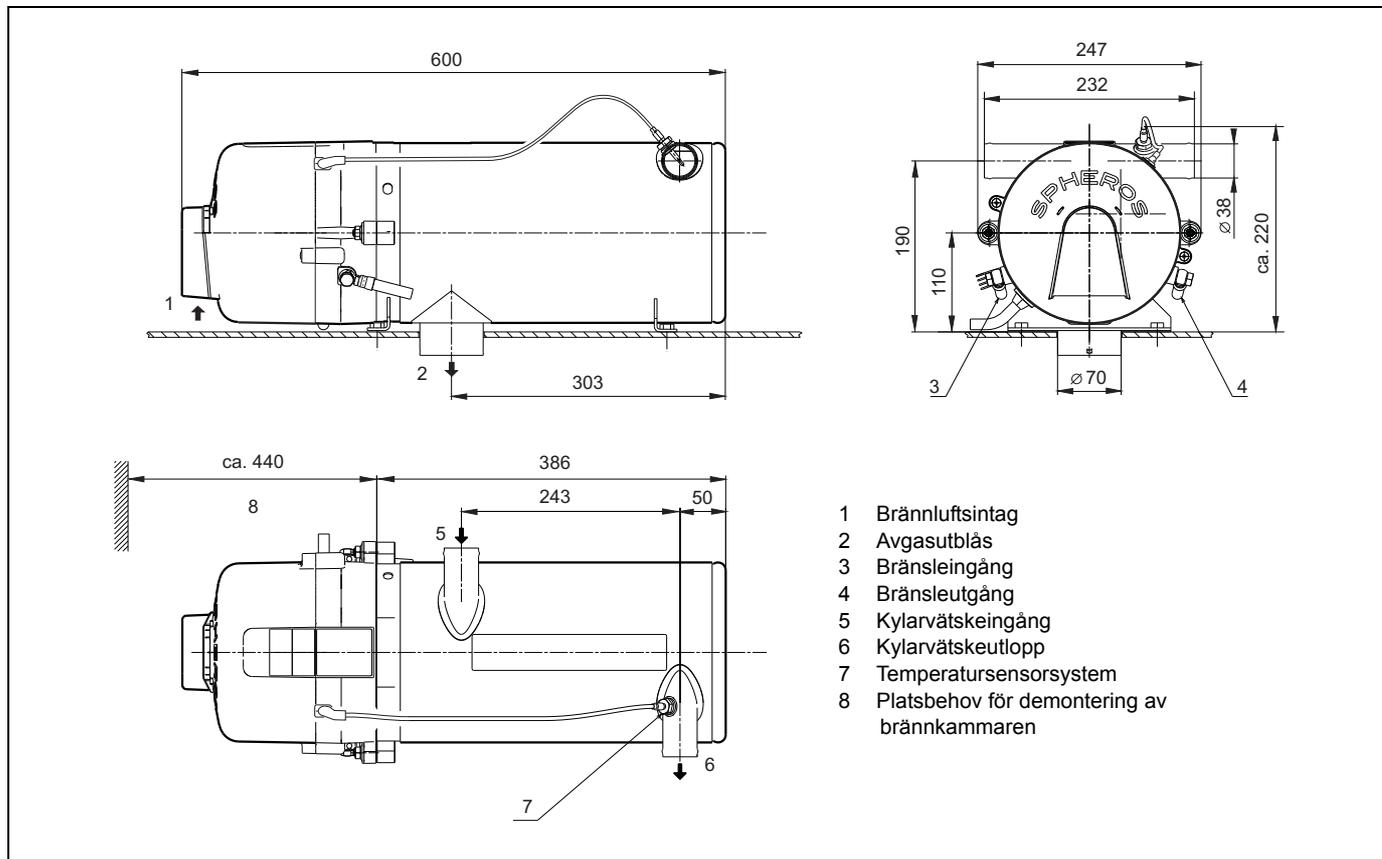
Värmarens dimensioner Thermo S 160/230/300/350/400 (horisontell montering)
